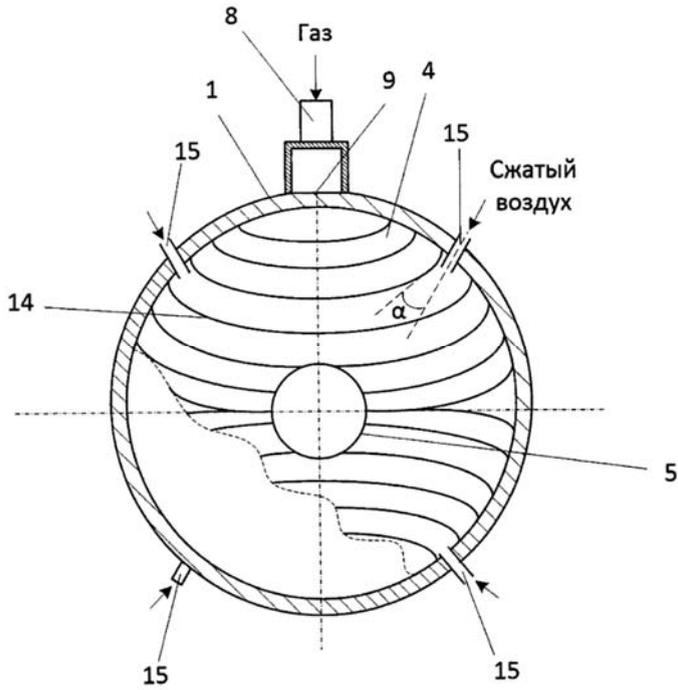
Профильный разрез ГУ новой конструкции типа ГП
